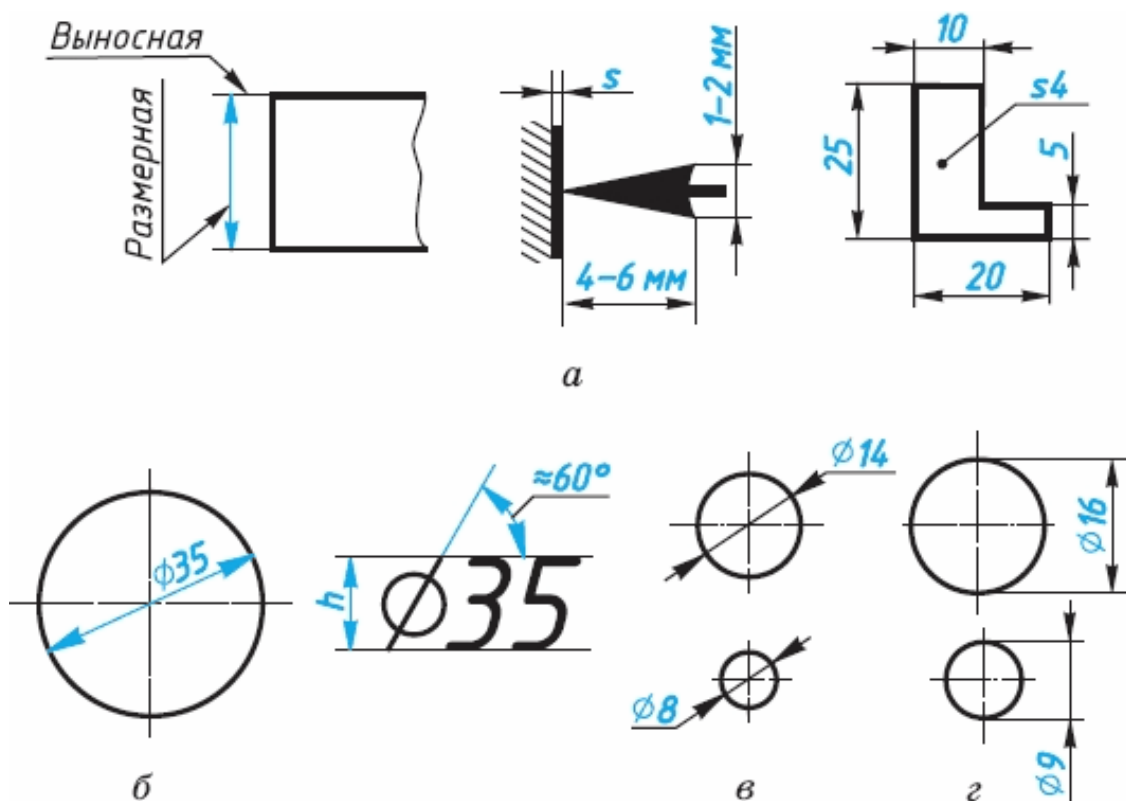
Креслення розмірних чисел та окремих знаків: а) стрілка розмірна, позначення товщини деталі «s4»; б) – г) - позначення діаметру кола на кресленні
